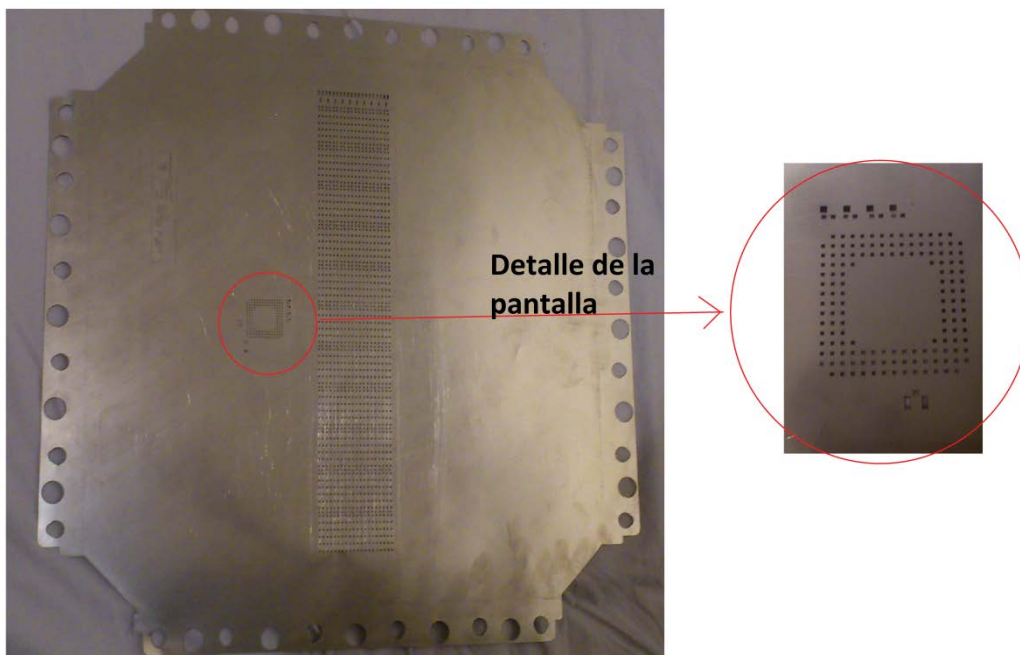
Pantalla desarrollada para deposición de la pasta sobre el PCB.
